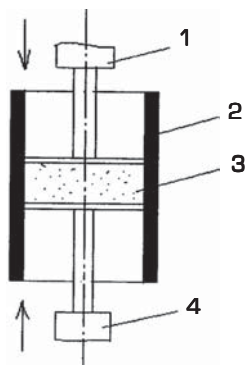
Схема двустороннего уплотнения: 1 – верхний пневмоцилиндр; 2 – гильза; 3 – образец смеси; 4 – нижний пневмоцилиндр
